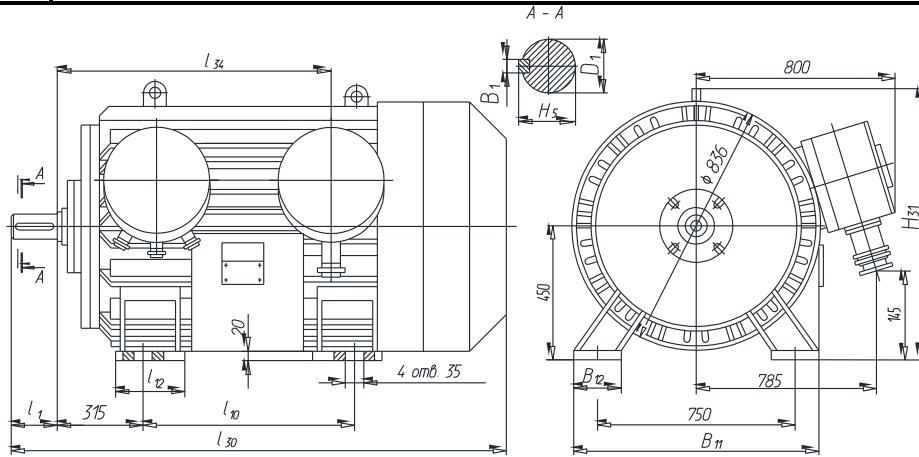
Габаритные и присоединительные размеры двигателей IM1001.
